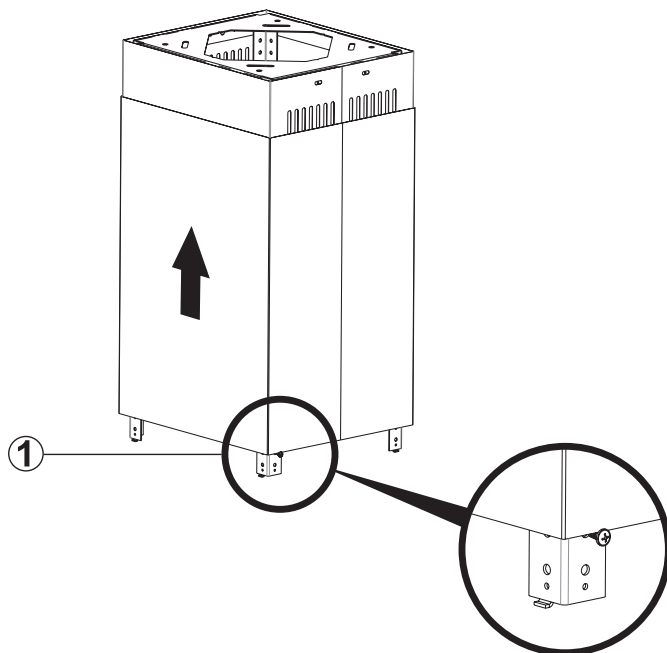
INSTALLAZIONE E COMPONENTI PARTE 3
